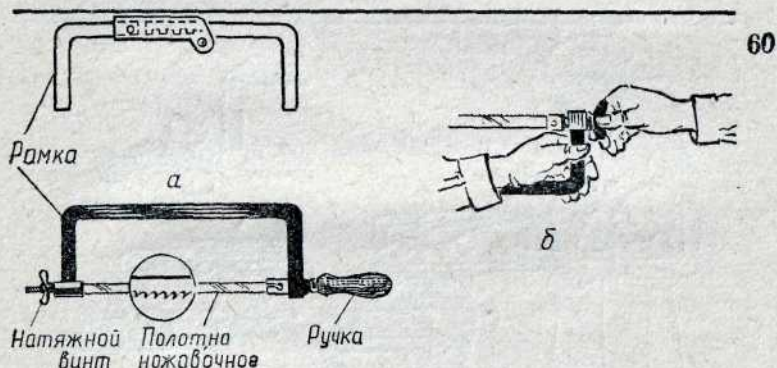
Ножовка слесарная: а — общий вид (вверху — разъемная рамка; внизу — неразъемная), б — натяжка ножовочного полотна,
